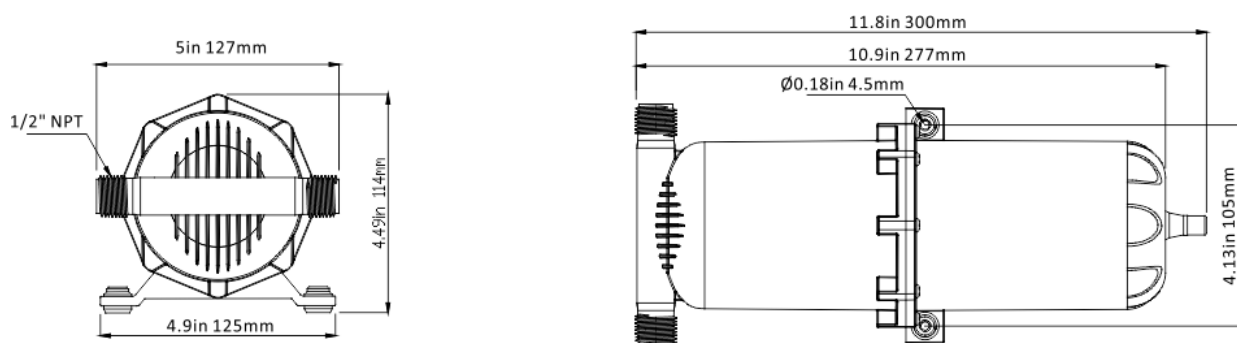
SFAT-100-125-01, габаритные размеры
